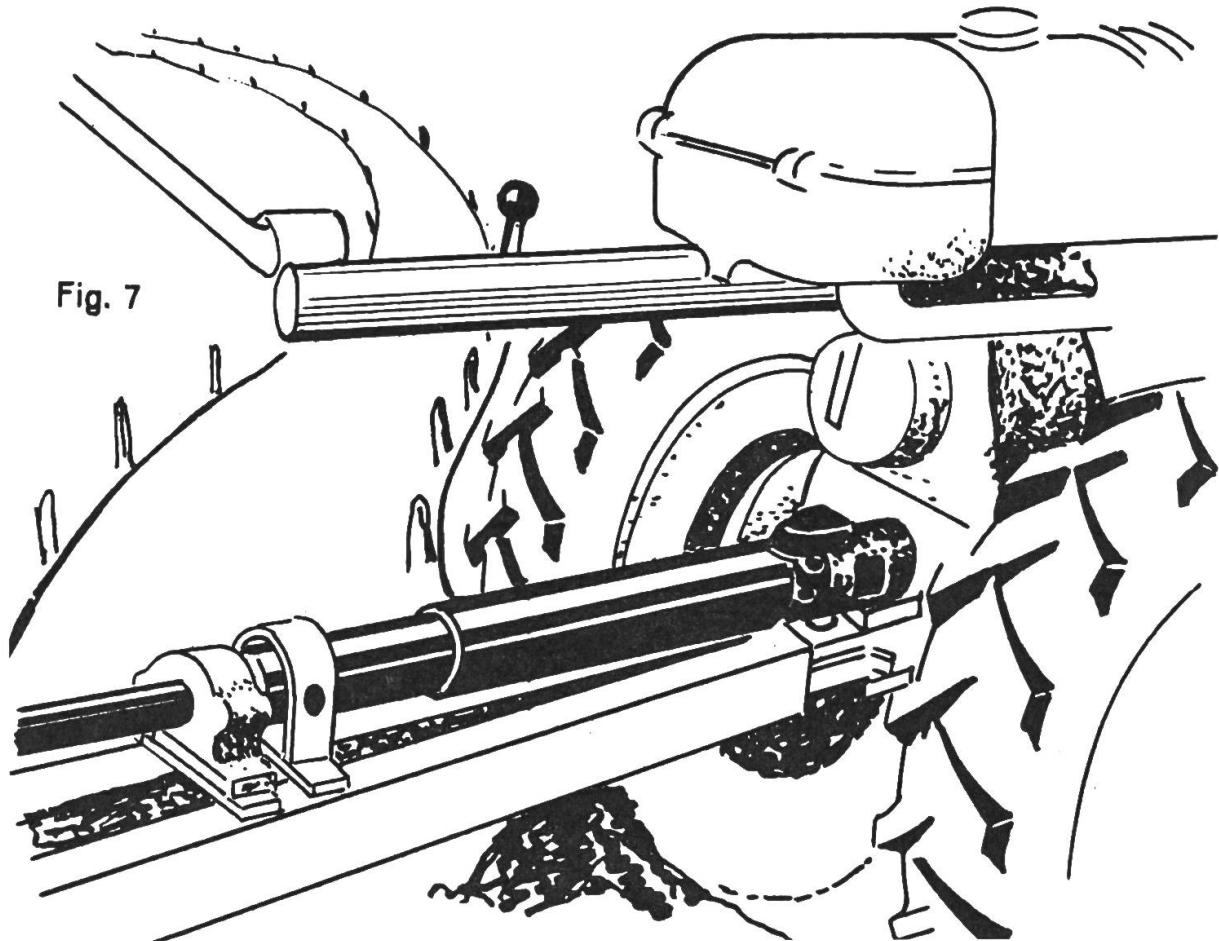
Ist die Kardanwelle über dem Chassis des Anhängers montiert, so können Beschädigungen beim Ueberfahren von Bodenwellen vermieden werden; die Führung der Kardanwelle unter dem Chassis bringt nachteilige Folgen mit sich.
